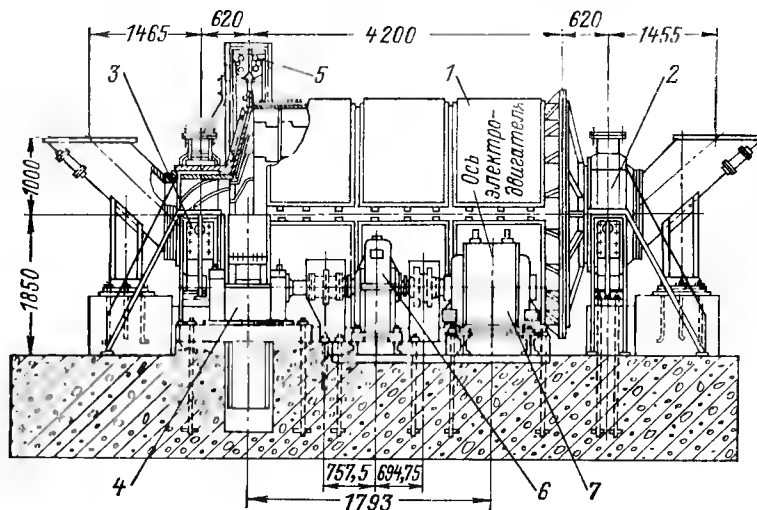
Шаровая барабанная мельница с редукторным приводом.
